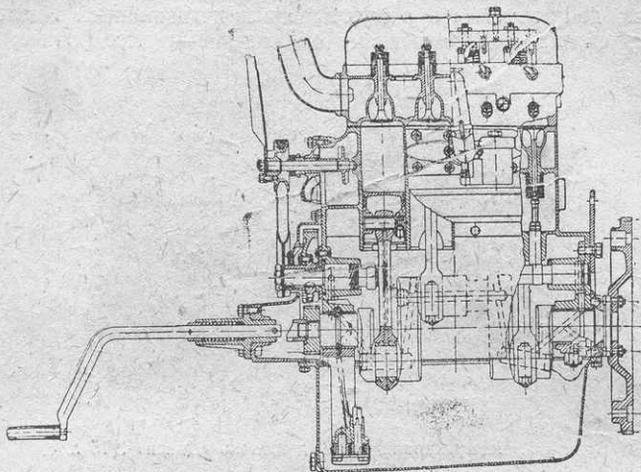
Продольный разрез четырехцилиндрового двигателя «Бреннабор» 6/25 л. с.
